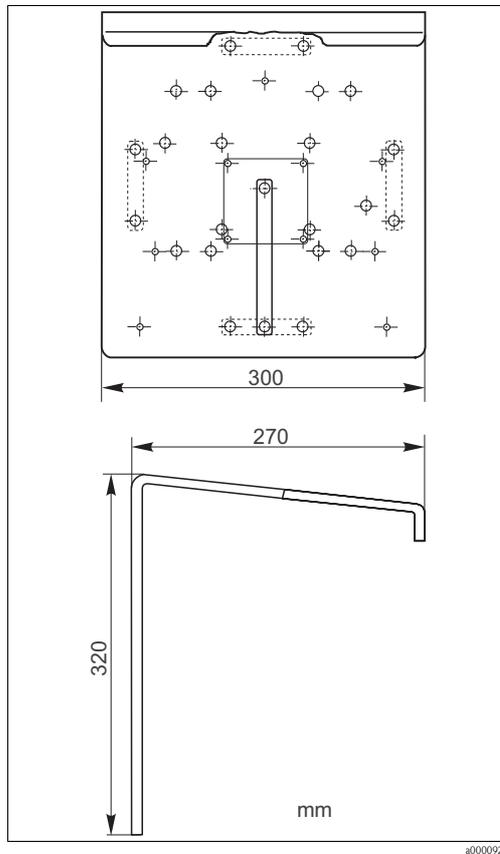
Tettuccio di protezione dalle intemperie CYY101
